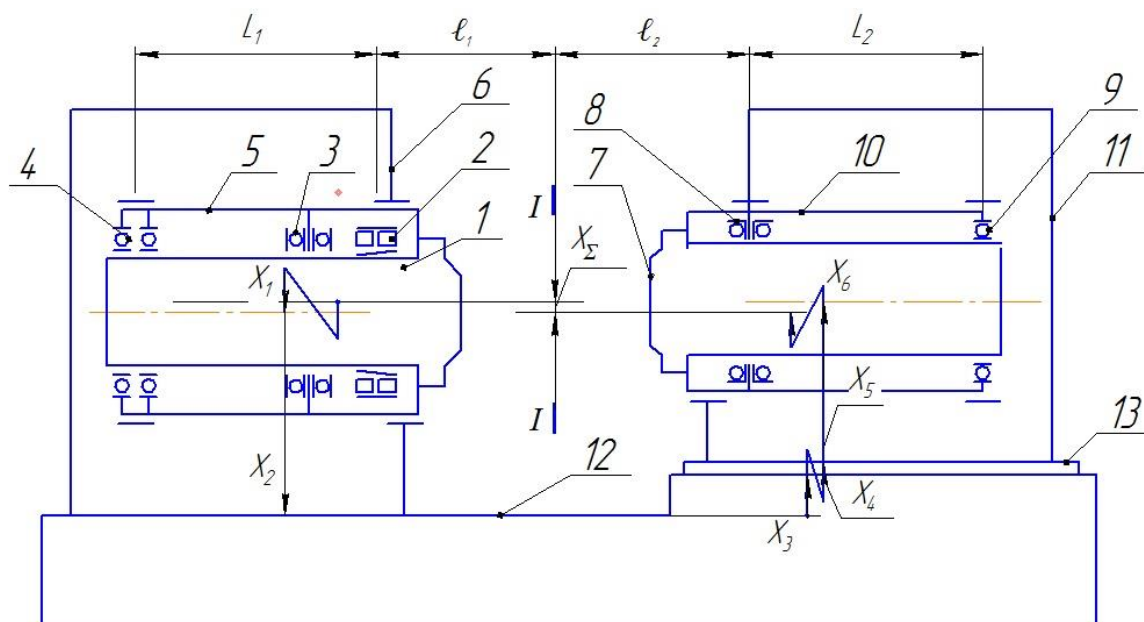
Компоновка соосных шпиндельных узлов металлорежущего станка
